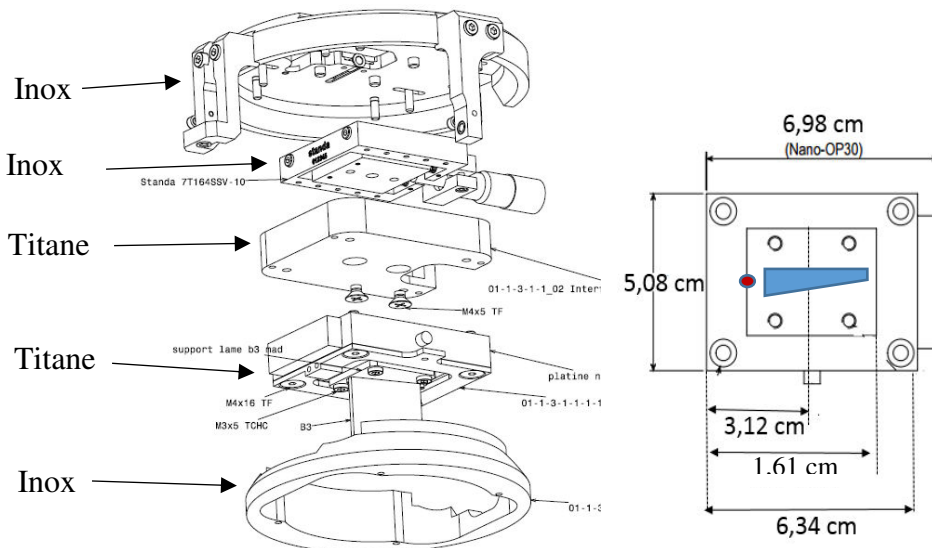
A gauche : vue éclatée du support mécanique de la lame B3. A droite : dimensions de la platine piezo-électrique. En rouge l'emplacement supposé du capteur de position.
